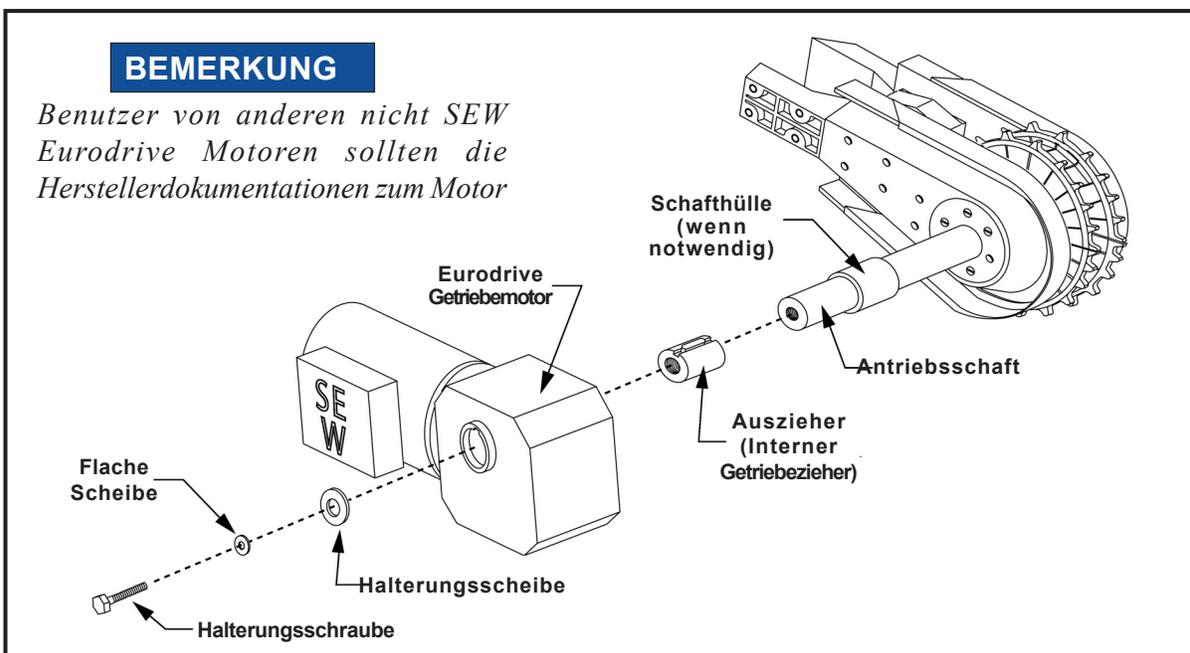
Montage des SEW Eurodrive Getriebemotors
